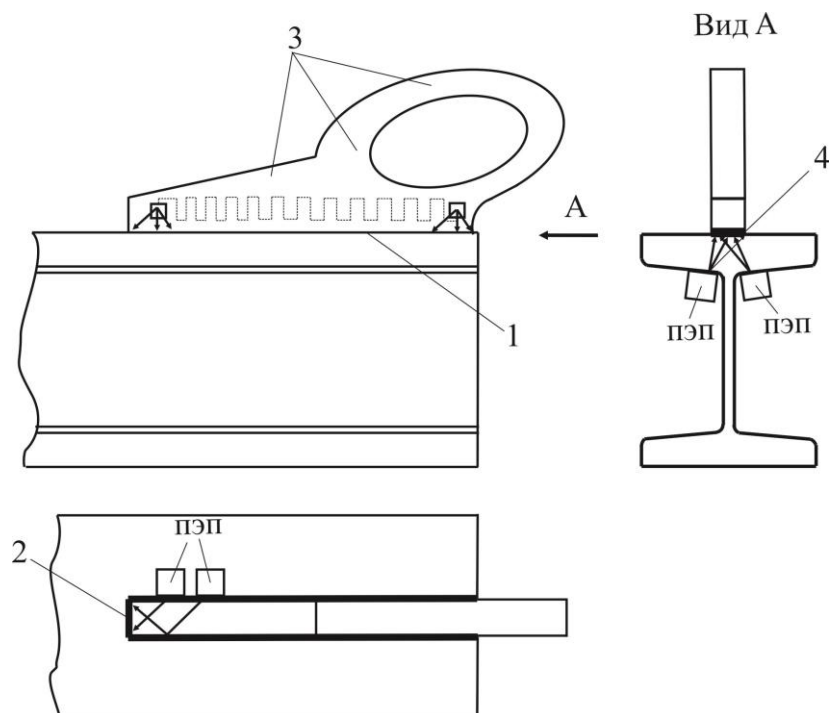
Схема УЗК сварных швов проушин монорельсовых балок
